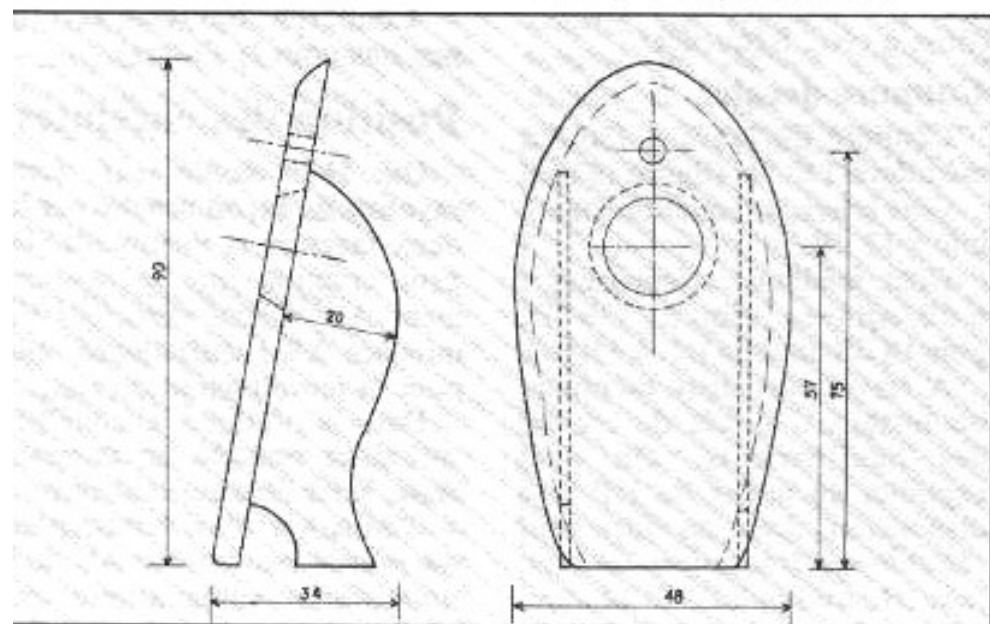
et 18 : Vue en coupe et vue de face du prototype 3.
